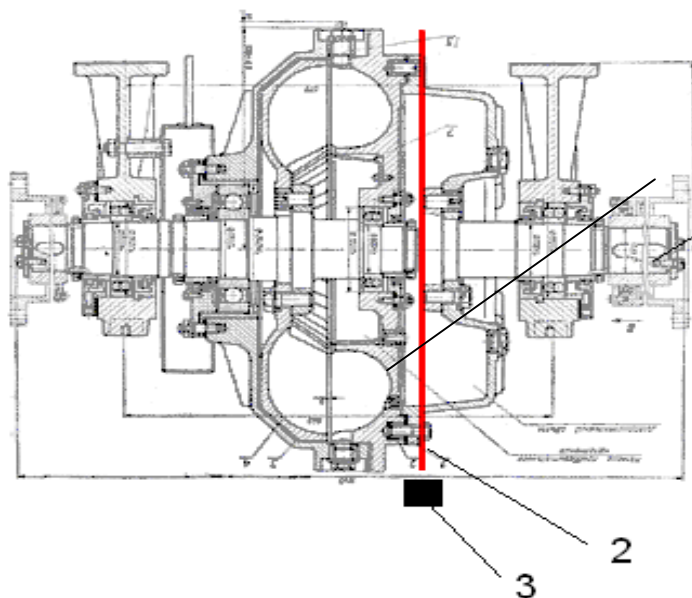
Общий вид гидромуфты с расположением датчика скорости.
